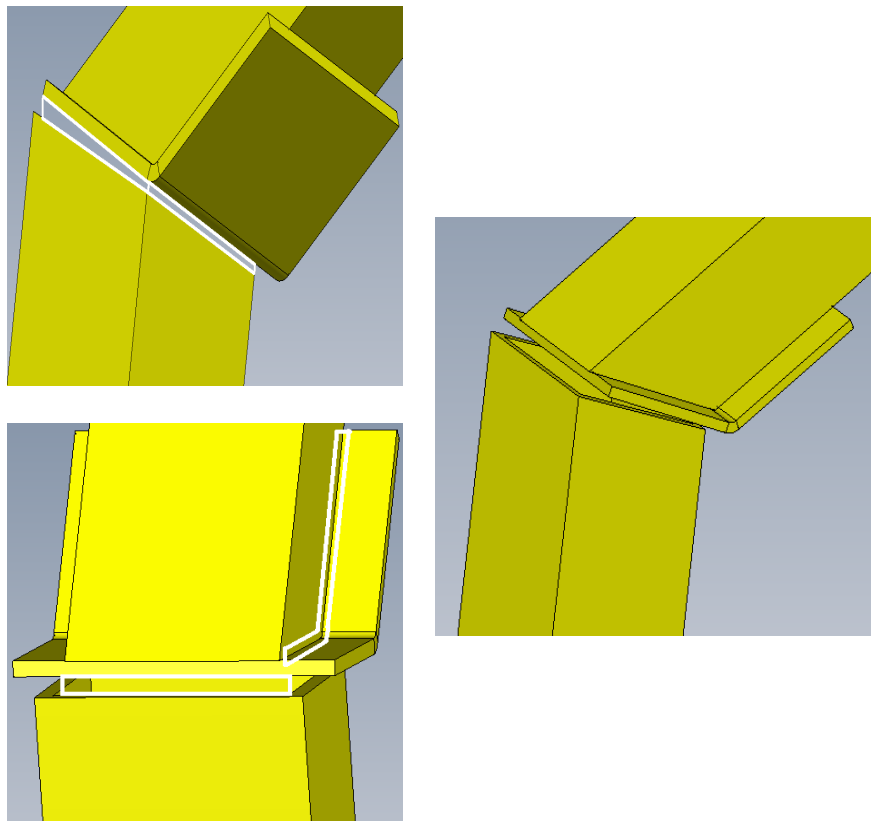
As zonas assinaladas possuem cordão de soldadura
